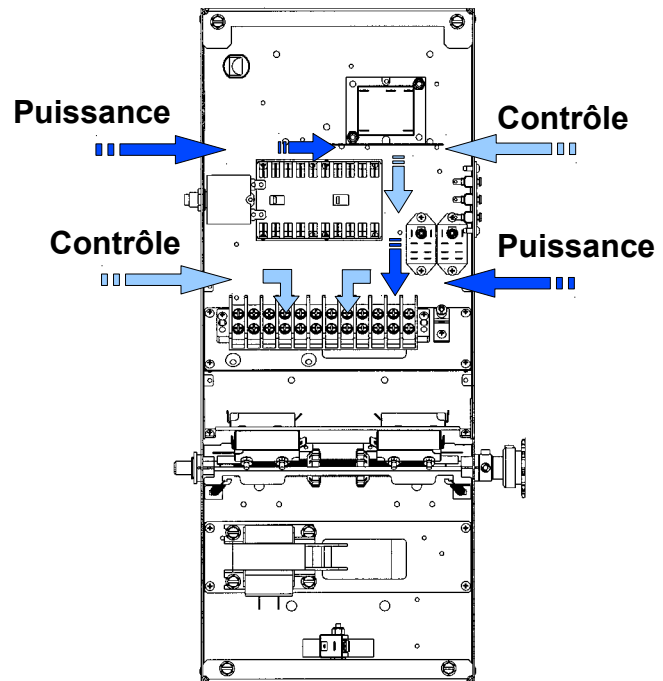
Branchement basse tension (contrôle) et haute tension (puissance)
